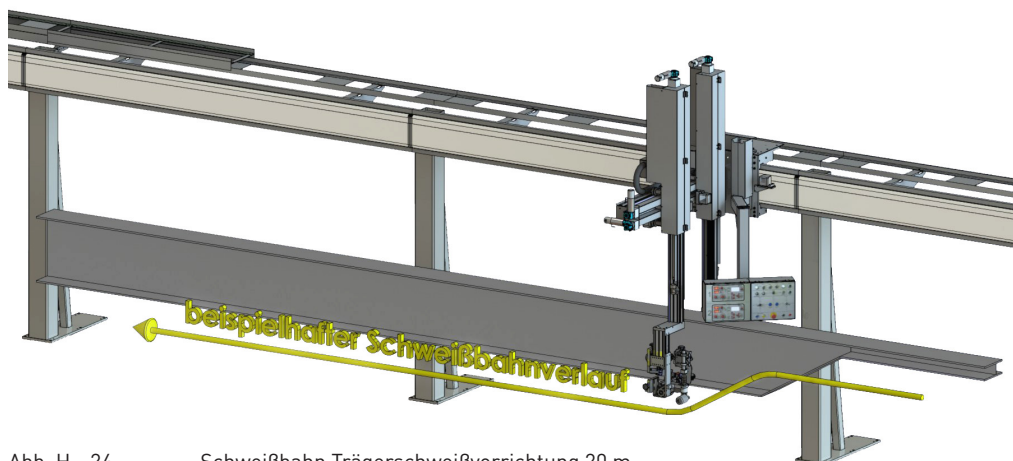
Schweißbahn Trägerschweißvorrichtung 20 m
